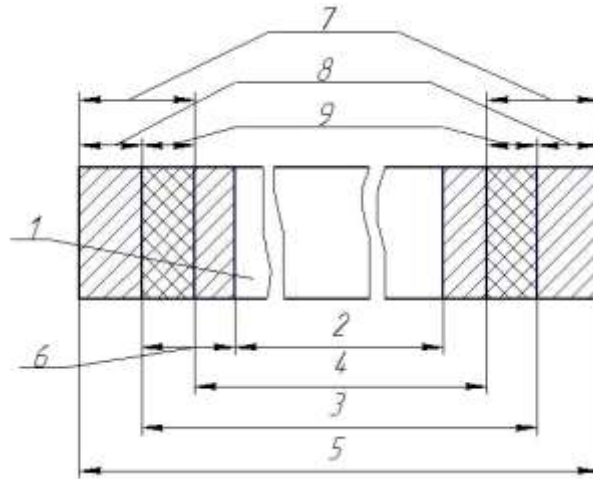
Взаємозв’язок між номінальними розмірами деталі та заготовки [4]:
